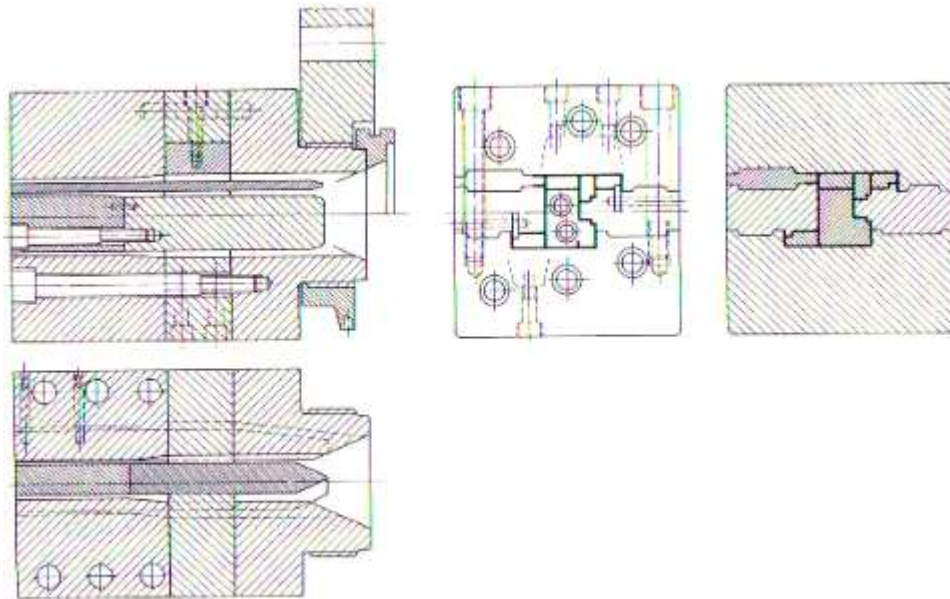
Typy hlav dle tvaru brzdného můstku [6]
